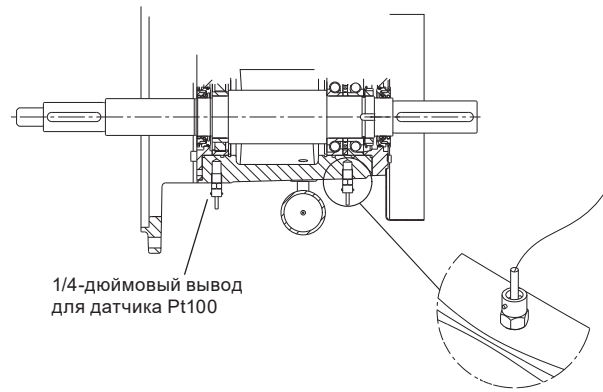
Датчики Pt100, установленные в корпус подшипников
